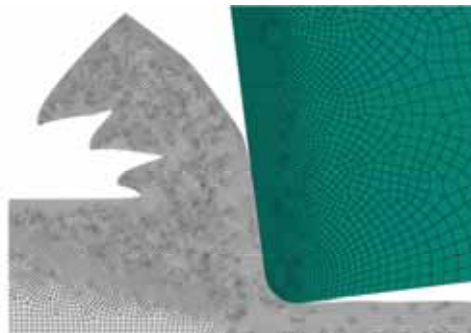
Lückenloser Kontakt zwischen Werkzeug und Werkstück
